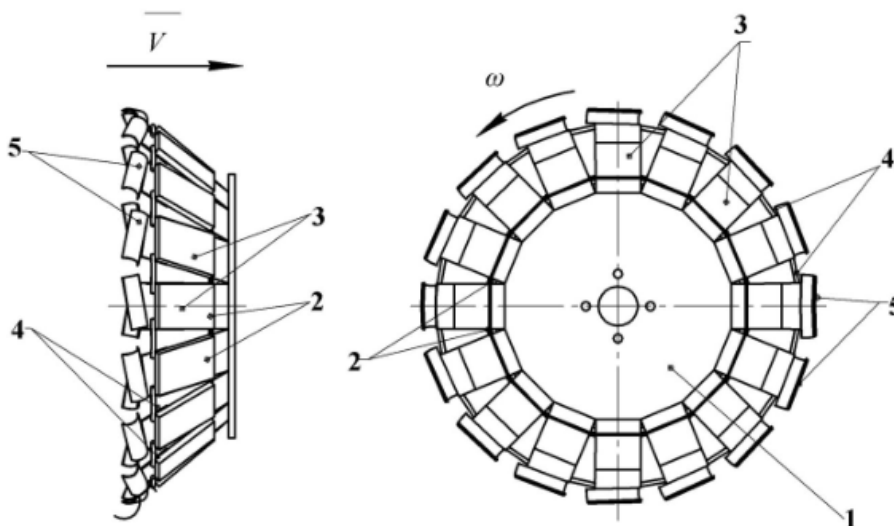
Конструктивна схема нового копірно-роторного відокремлювача гички.
